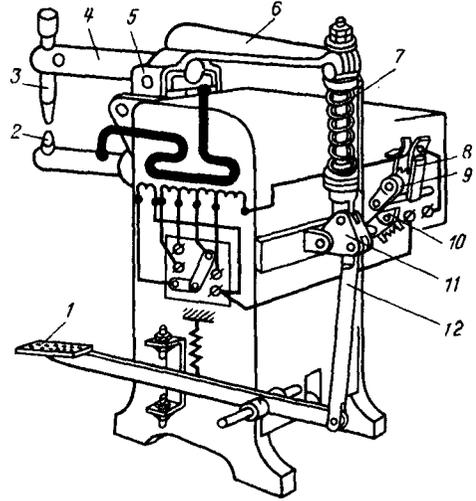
Машина для точечной сварки АТП-25
